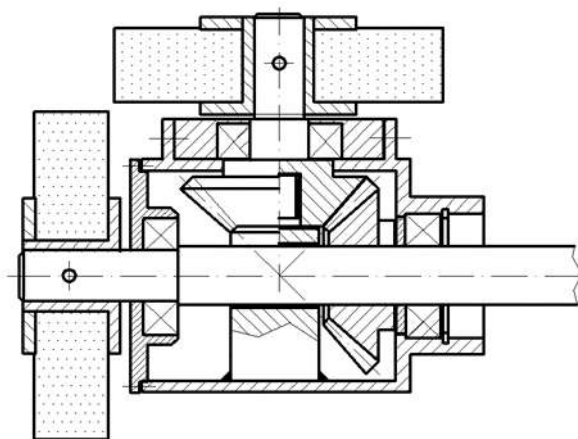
Конструкція шліфувальної головки з двома абразивними кругами
